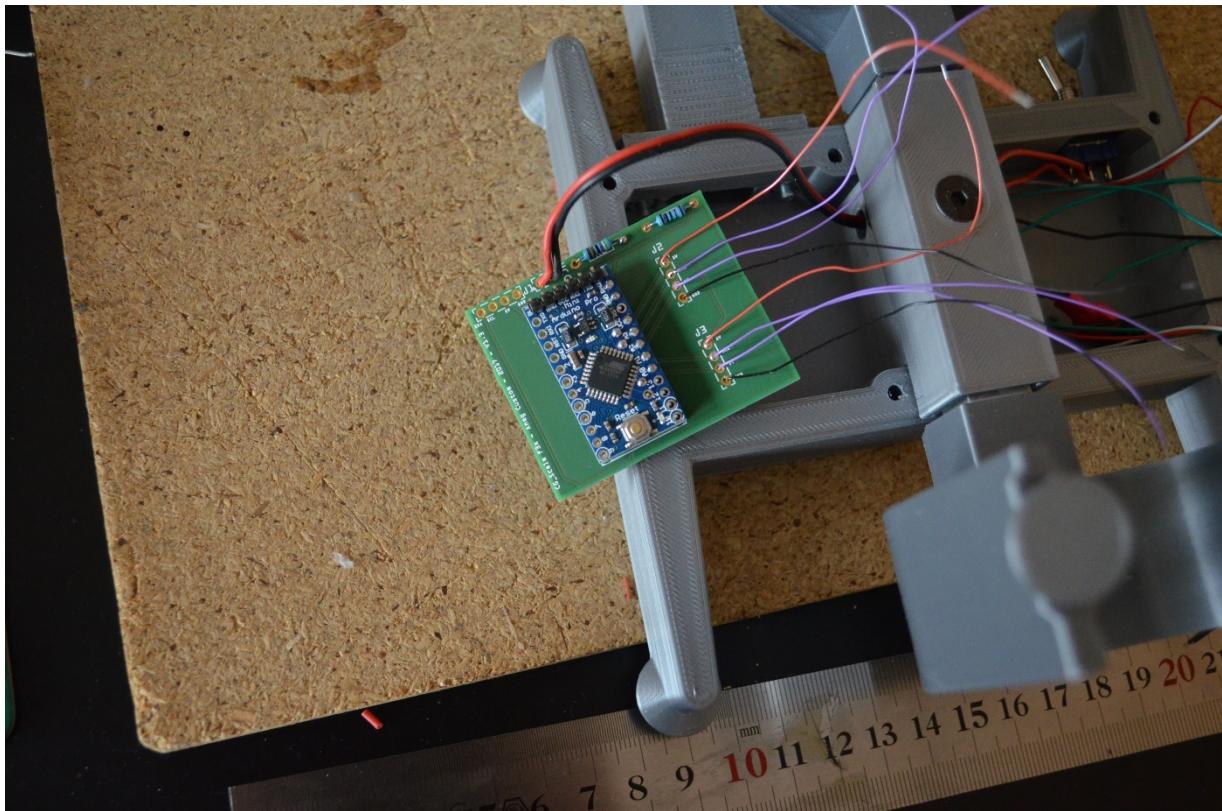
Etape 8 – souder les 8 brins de Kynar sur le PCB.
